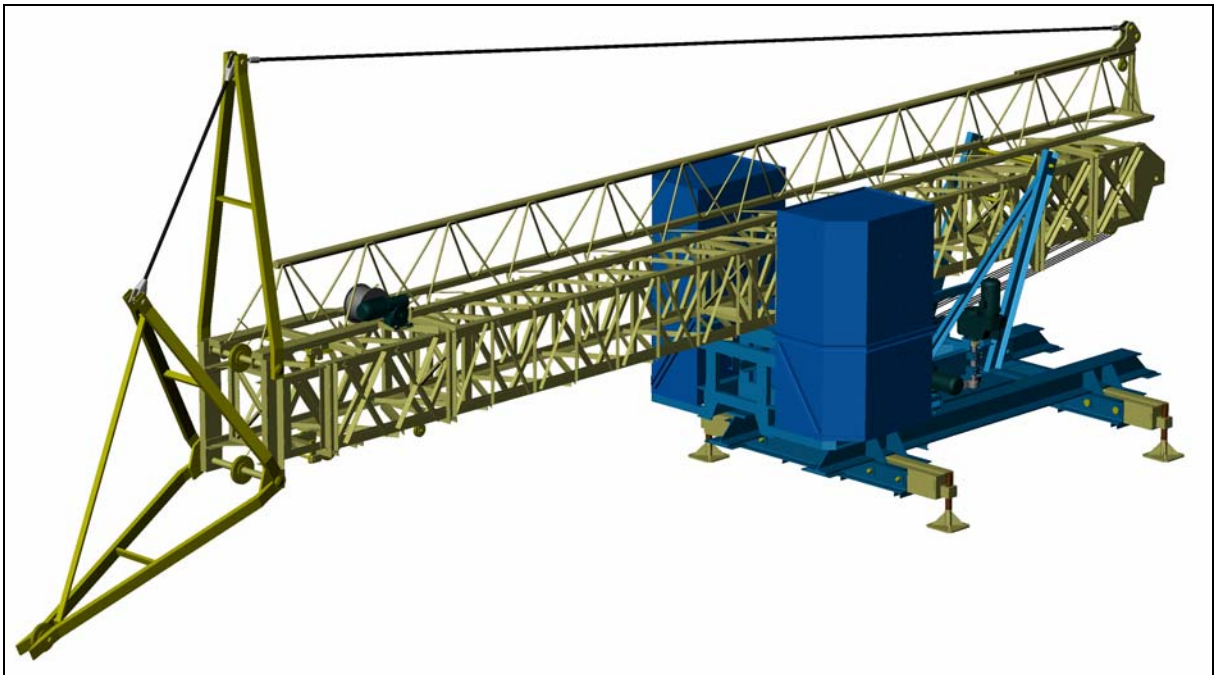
Vista de la grúa con las eslingas 2 y 3 montadas
